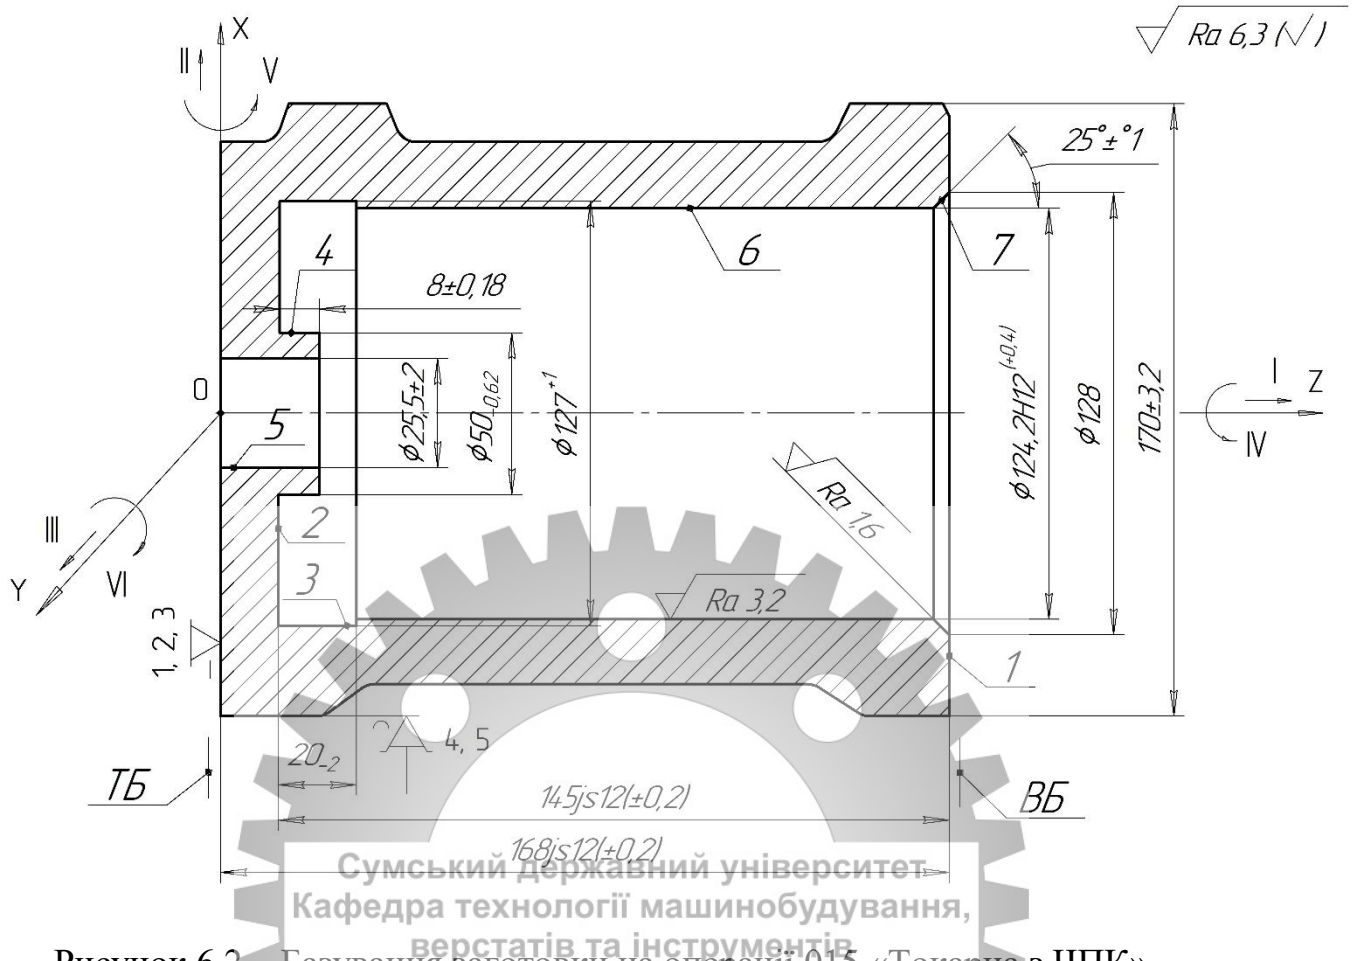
Базування заготовки на операції 015 «Токарна з ЧПК»
